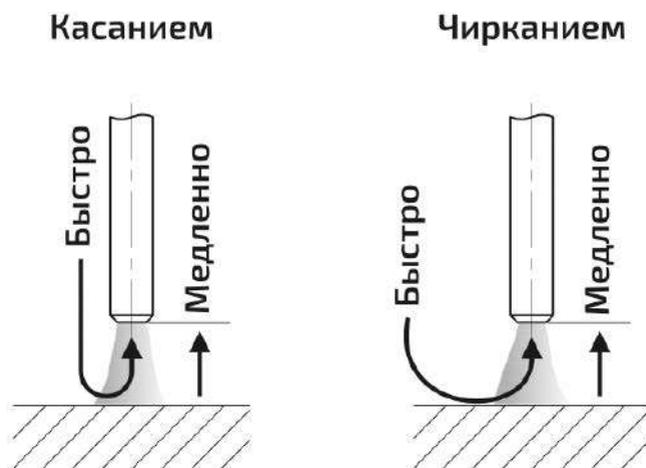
Способы зажигания сварочной дуги.
